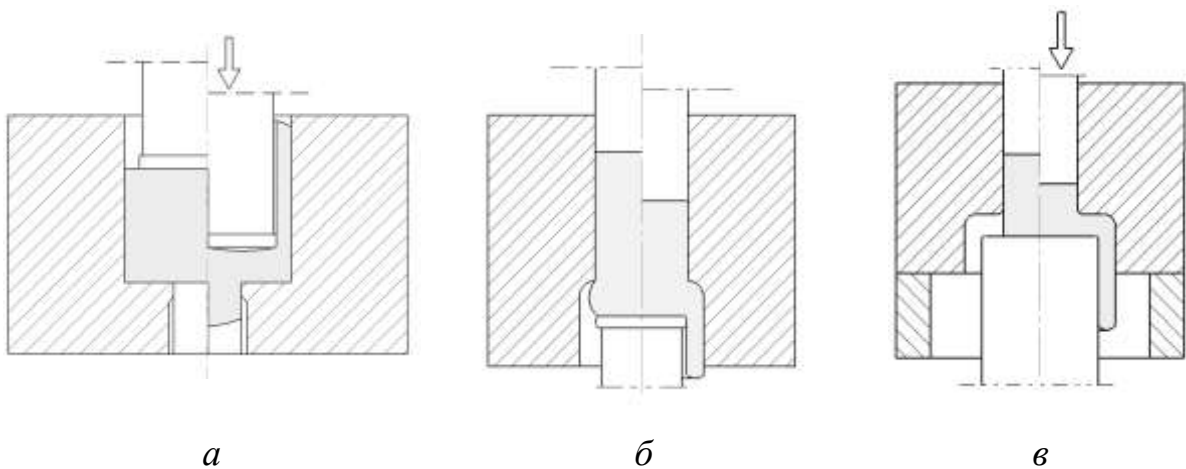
Схеми комбінованого видавлювання деталей типу стаканів з зовнішніми відростками
